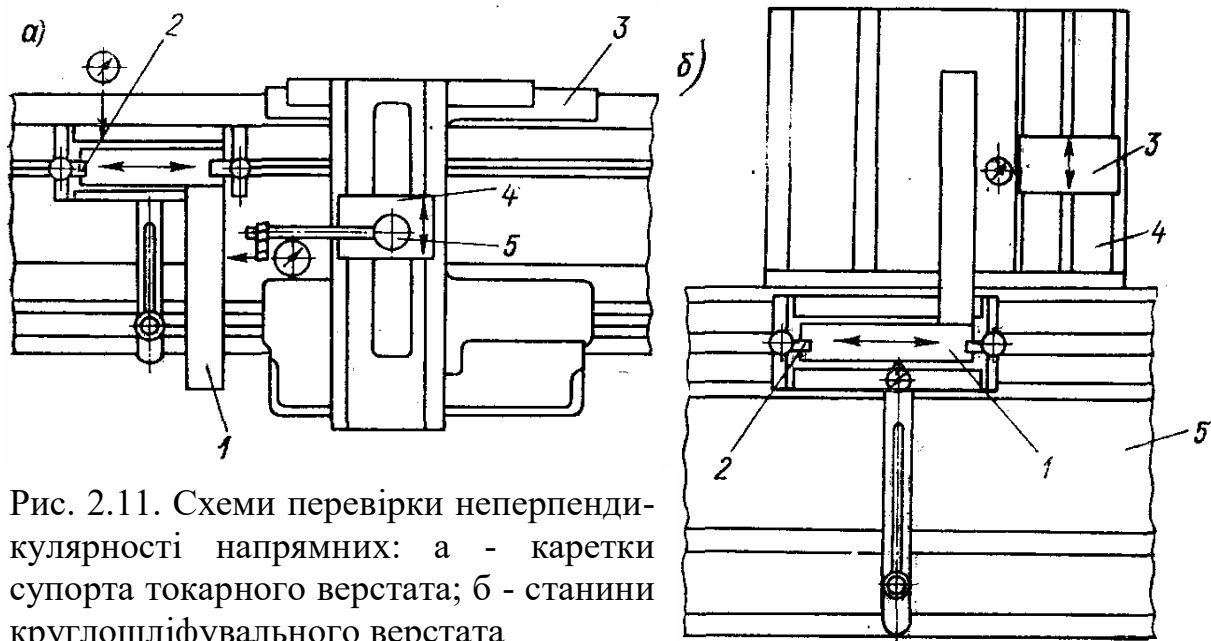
Схеми перевірки неперпендикулярності напрямних: а - каретки супорта токарного верстата; б - станини круглошліфувального верстата
